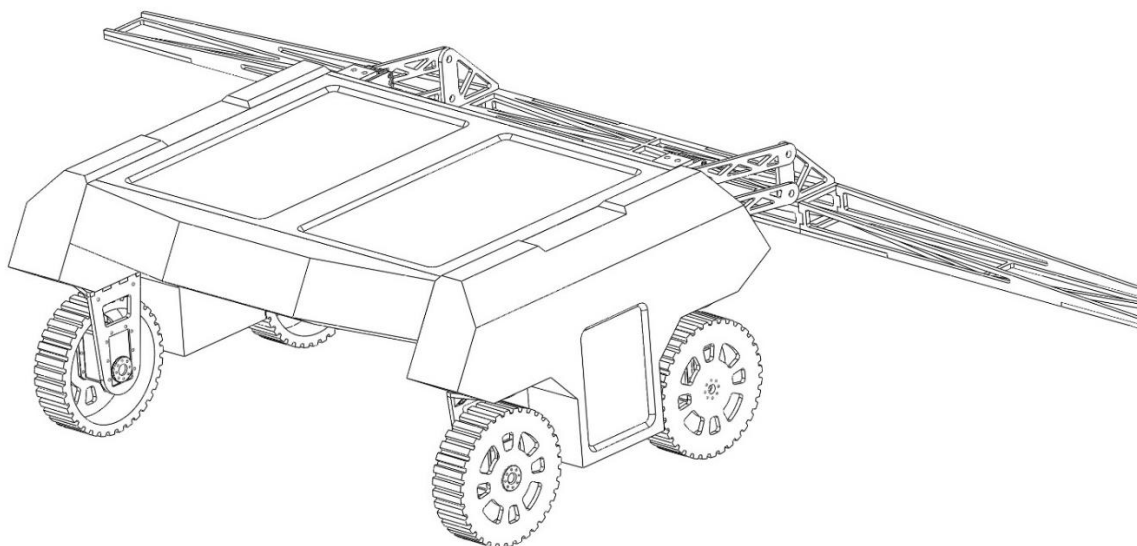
Модель прототипу разом із матрицями корпусу
